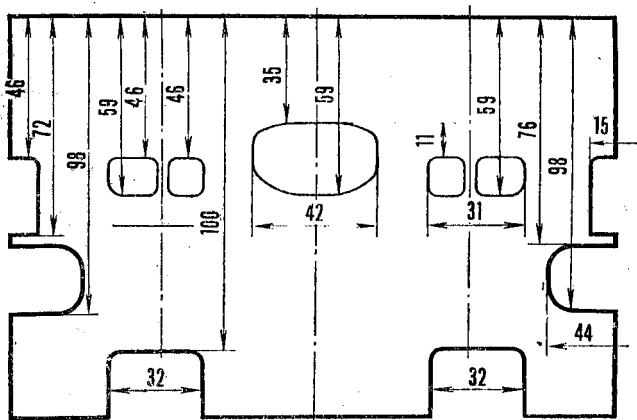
Развертка цилиндра форсированного двигателя ИЖ-«Юпитер-2»
